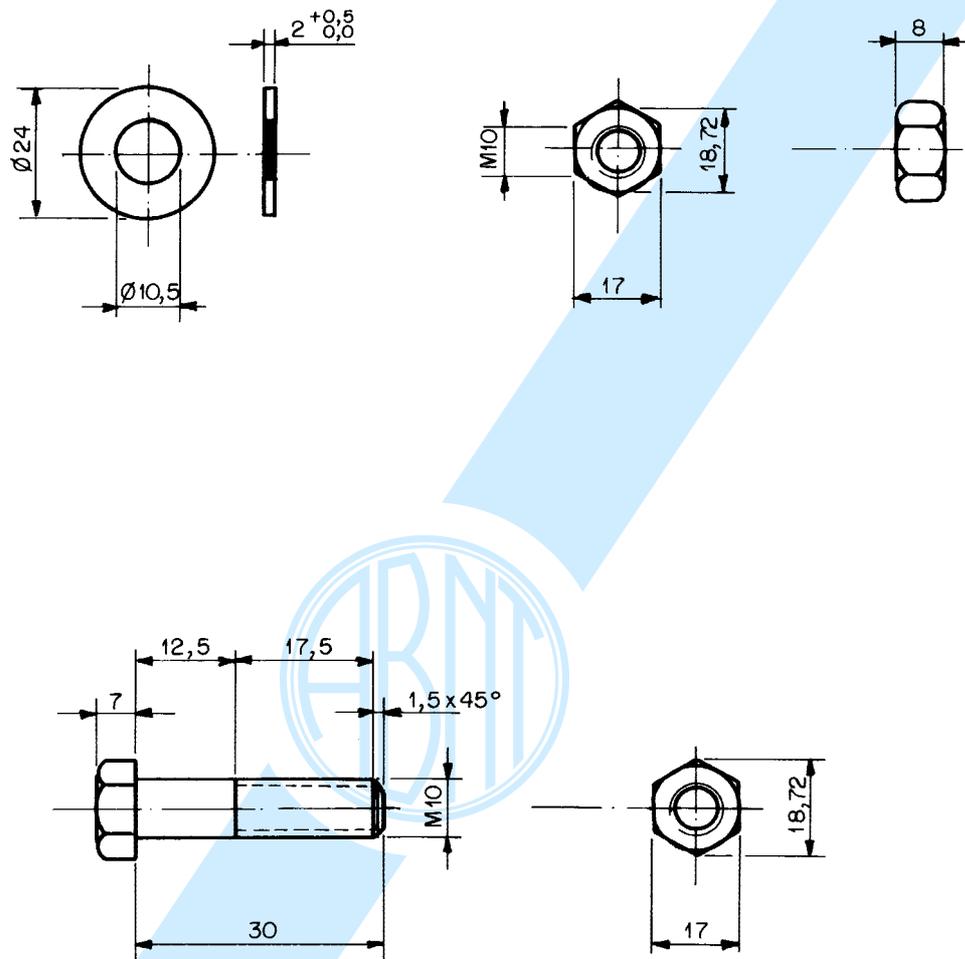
Conjunto parafuso M10, com porca e arruela
